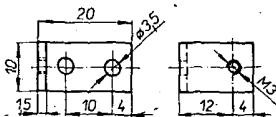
Skříňka zesilovače; a) horní viko, b)
